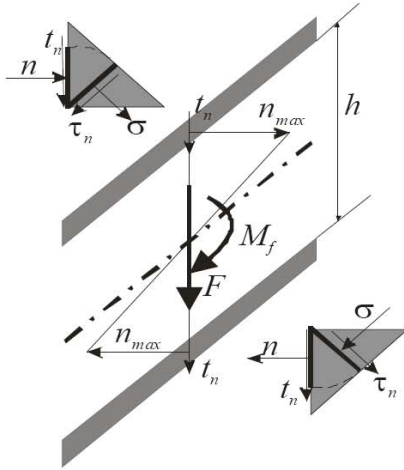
SOLDADURAS FRONTALES TRANSVERSALES SOMETIDAS A FLEXIÓN
